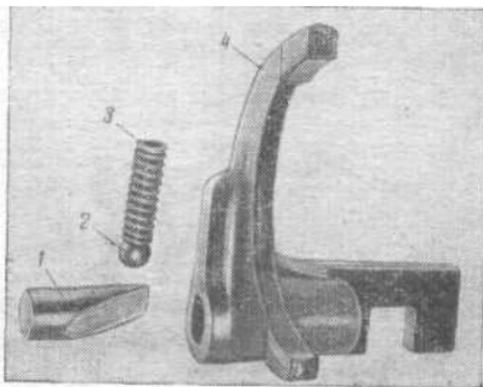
Клиновья оправка для сборки деталей фиксатора вилок переключения передач
